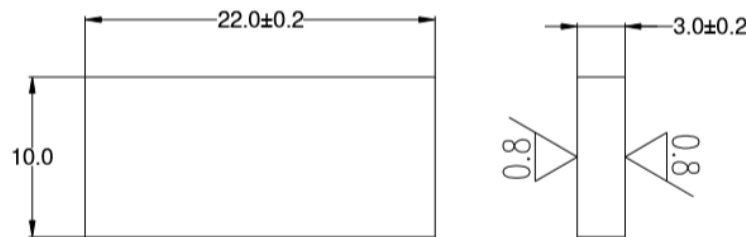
Desenho técnico do componente de metal duro K30, fornecido pela Frezite.
